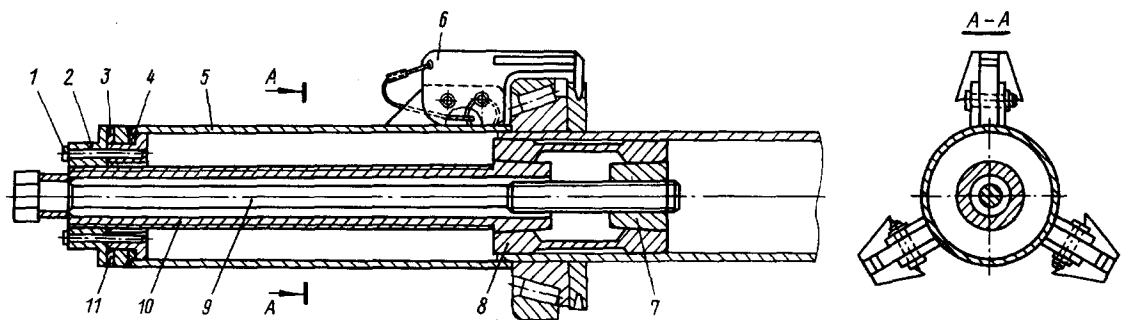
Приспособление для монтажа и демонтажа подшипников основных
